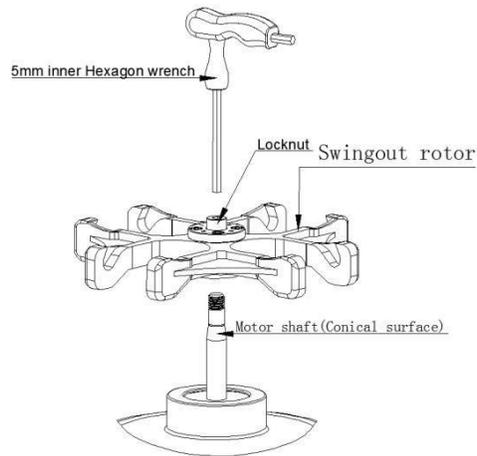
Imagen de la instalación del rotor angular (de arriba hacia abajo: llave hexagonal interna de 5 mm; tuerca de seguridad, rotor Swingout, motor del husillo (superficie cónica))
